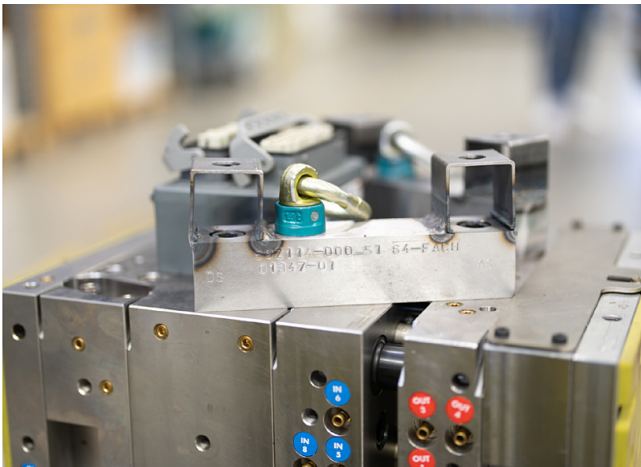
Spritzgusswerkzeug mit Werkzeugbrücke – gut erkennbar, die Bügel für die Unverlierbarkeit der Schrauben
